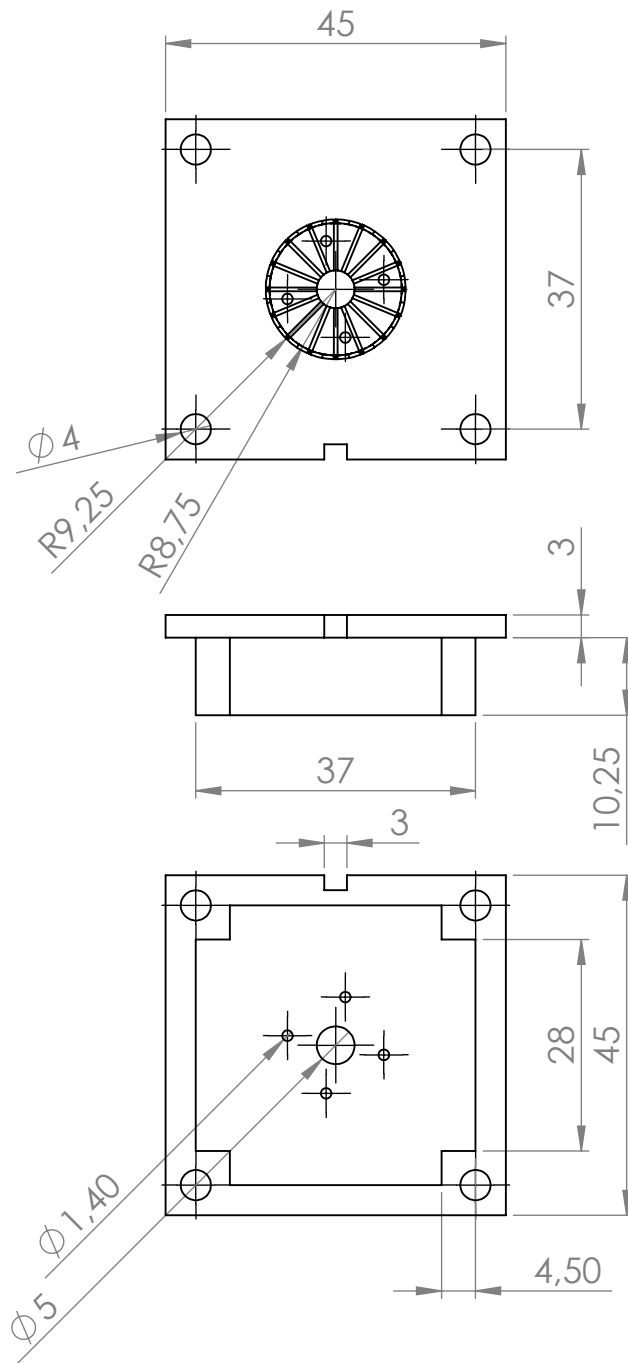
Diseño del molde para enmallado interno del *Robot Biaxial* parte B
